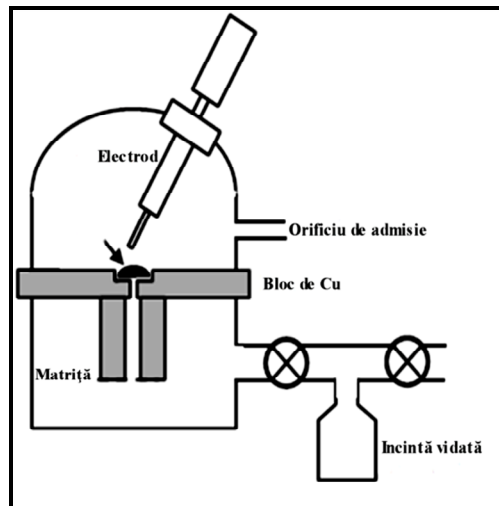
Instalația de turnare prin aspirație (prelucrată din [53])
